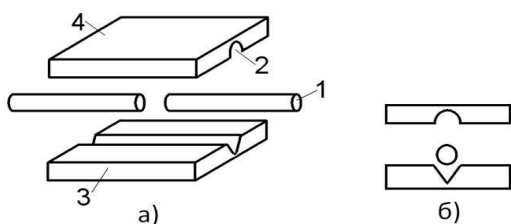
Соединение с помощью пластин: а) с канавками круглой формы; б) с V-образными канавками; 1 – волокно; 2 – канавки; 3 – пластина; 4 – крышка
